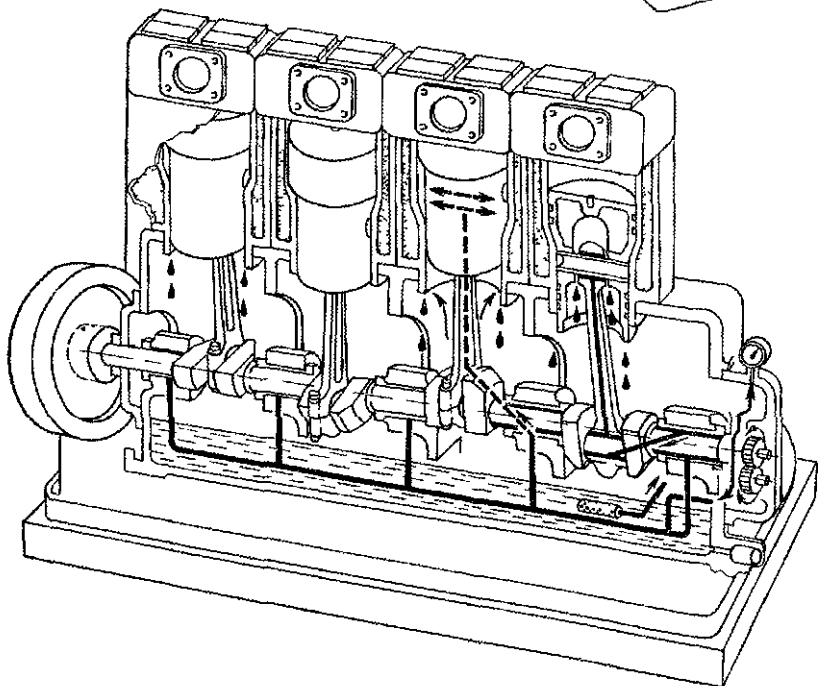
Смазка механизма движения под давлением, а цилиндров — разбрызгиванием
